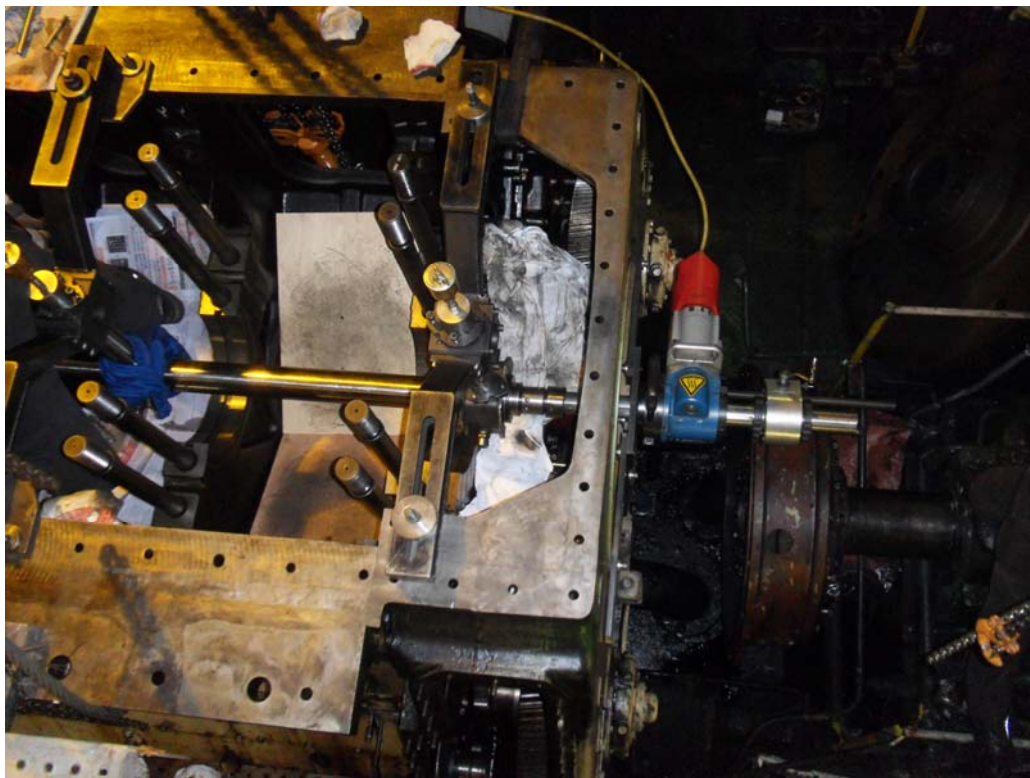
Центрирующая штанга для крепления инструмента и протачивания постелей подшипников
